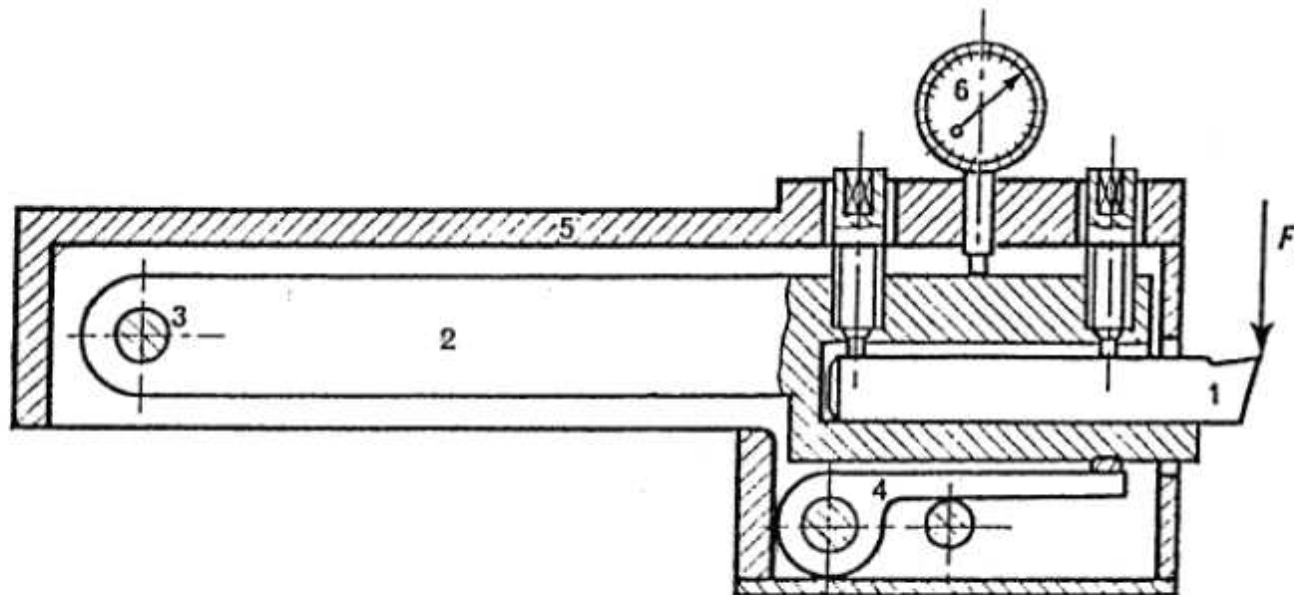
Dinamometro a schema meccanico; 1. Utensile; 2. Leva; 3. Fulcro; 4. Molla di reazione; 5. Corpo del dinamometro; 6. Comparatore millesimale; F_t , Forza principale di taglio.
